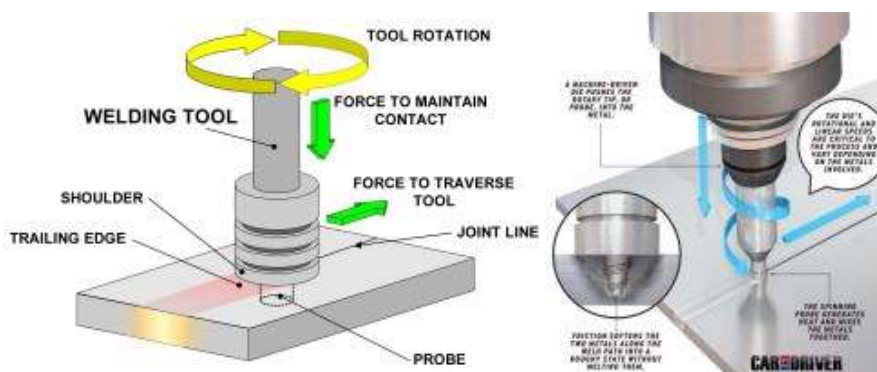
Identificación de los componentes de una soldadura FSW
